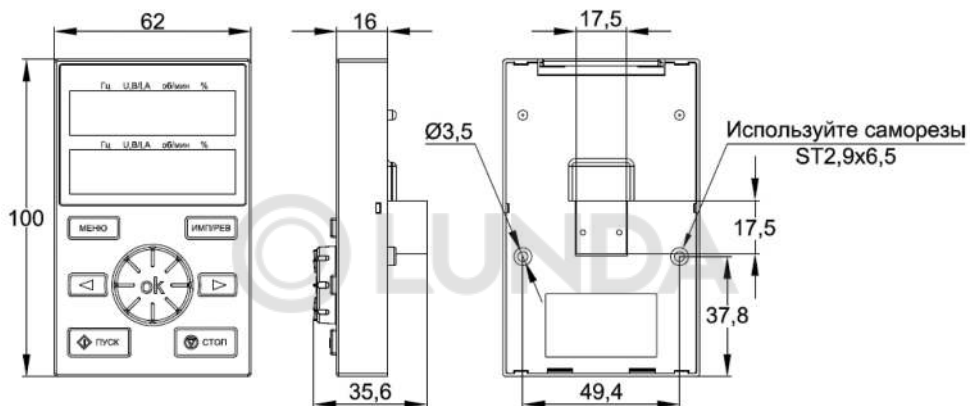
Габаритные размеры и размеры отверстий внешней цифровой двухстрочной панели управления (единица измерения – мм)
